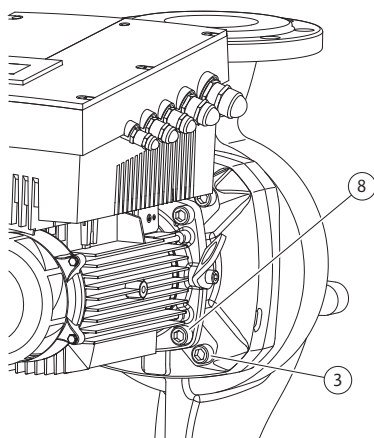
Fixarea opțională a ansamblului motor cu rotor hidraulic
